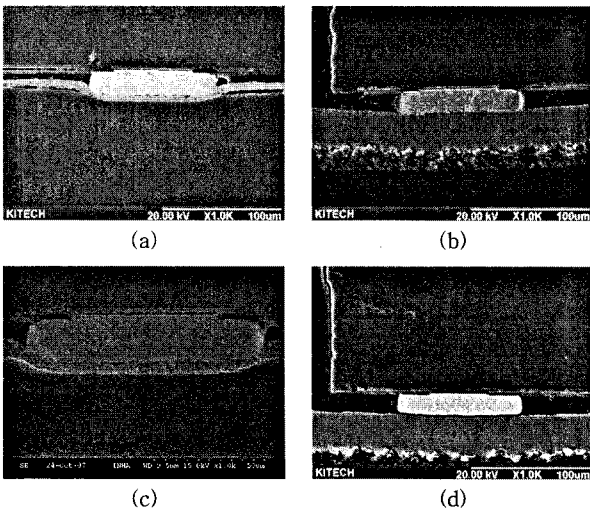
안테나 재질 및 ACP (또는 filler) 종류에 따른 접합부의 이미지: (a) Ag ink 안테나 상에 구형 Ag filler, (b) Cu 재질 안테나 상에 구형 Ag filler, (c) Ag ink 안테나 상에 Au/Ni coated polymer filler, (d) Cu 재질 안테나 상에 Au/Ni coated polymer filler.
